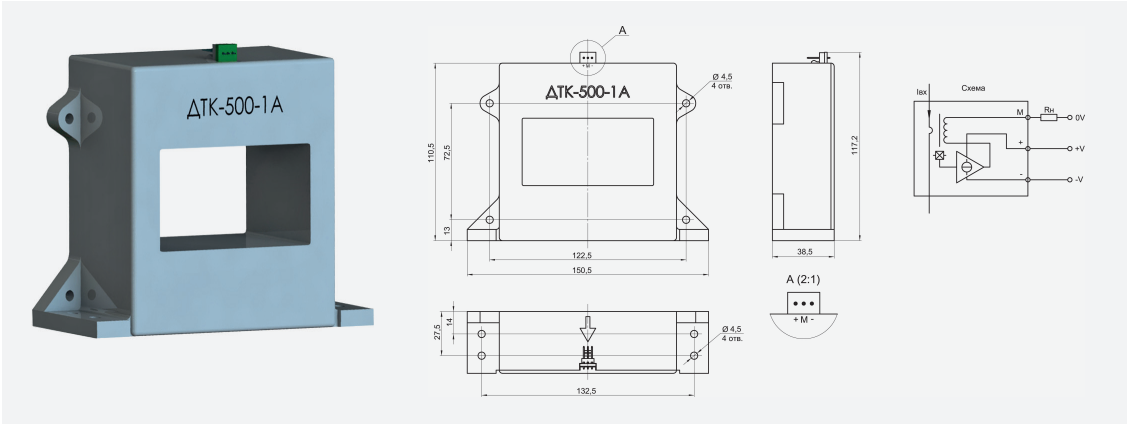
Внешний вид, габаритные размеры и схема измерительного преобразователя ДТК-500-1А
